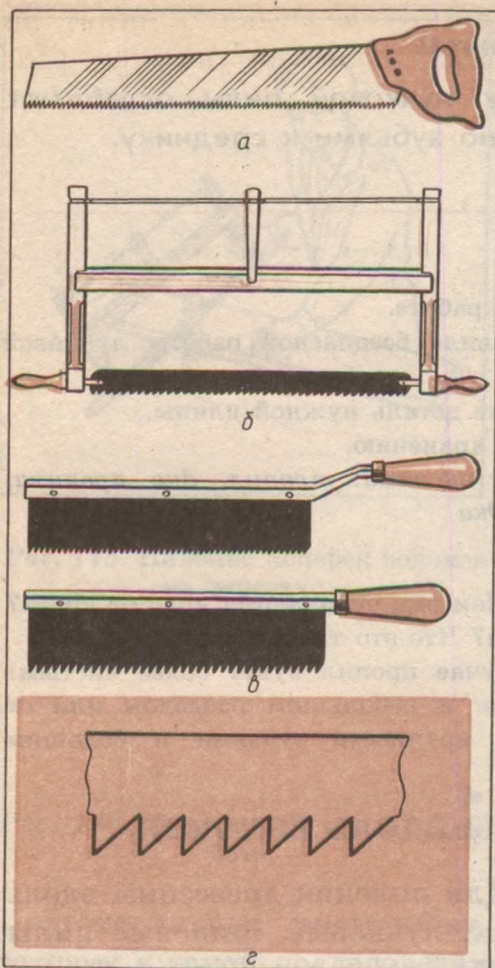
Пилы для пиления древесины вдоль волокон: а — ножовка; б — лучковая; в — шиповая; г — форма зубьев продольной пилы.
